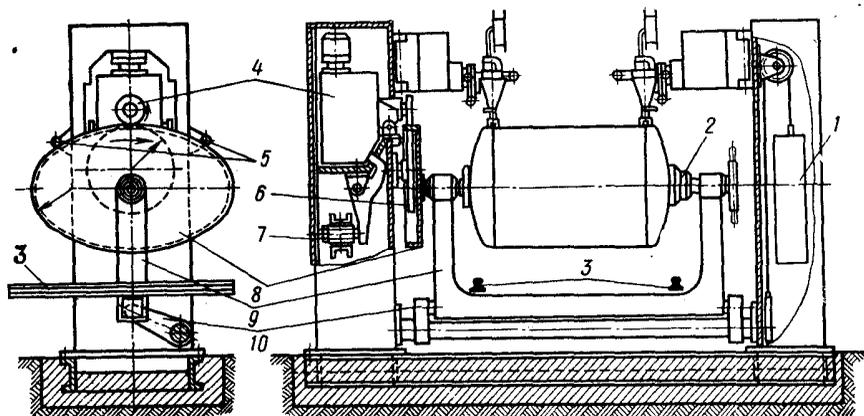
Схема станка для автоматической сварки овальных сосудов
